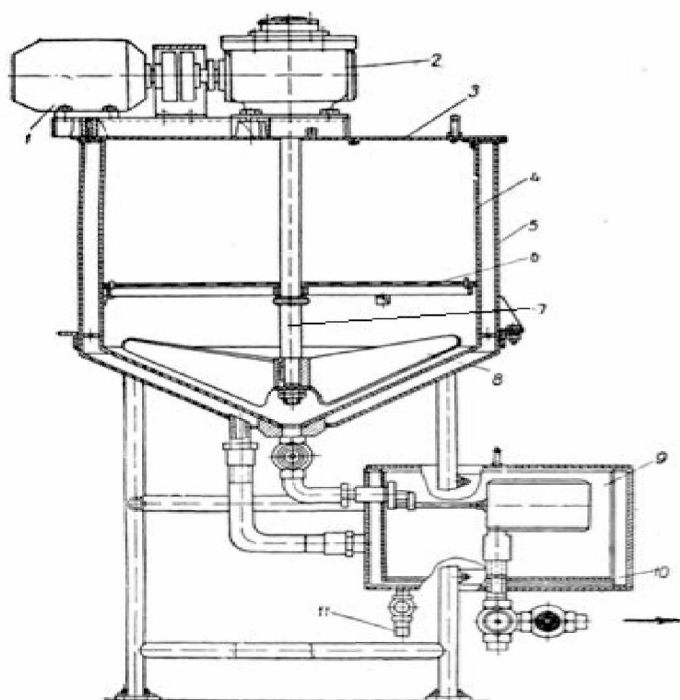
Апарат Х-15 для розтоплення жиру: 1 – двигун; 2 – редуктор; 3 – відкидна кришка; 4 – бак; 5 – водяна сорочка; 6 – решітка; 7 – вал; 8 – конусні лопаті; 9 – бачок постійного рівня з поплавковим пристроєм; 10 – водяна сорочка.
